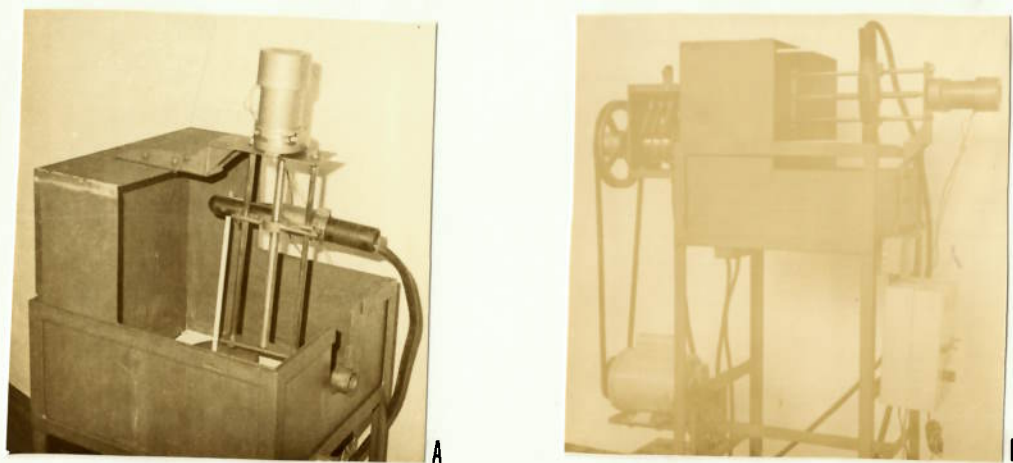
Detalhe do recipiente de coleta das gotas. Em (a) vê-se o recipiente para soldagem na posição plana e em (b) para a o não plana.
